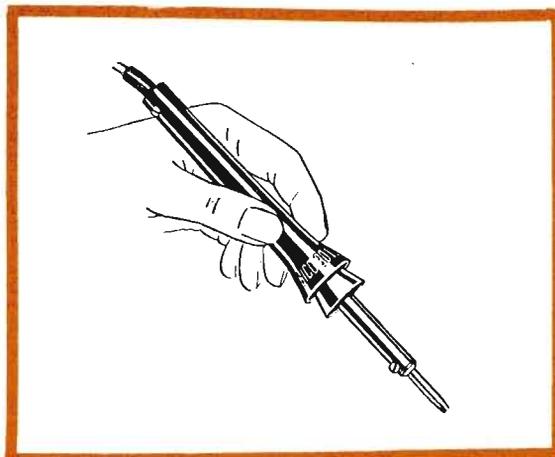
Questo è il sistema corretto di impugnatura di un saldatore per circuiti stampati.
